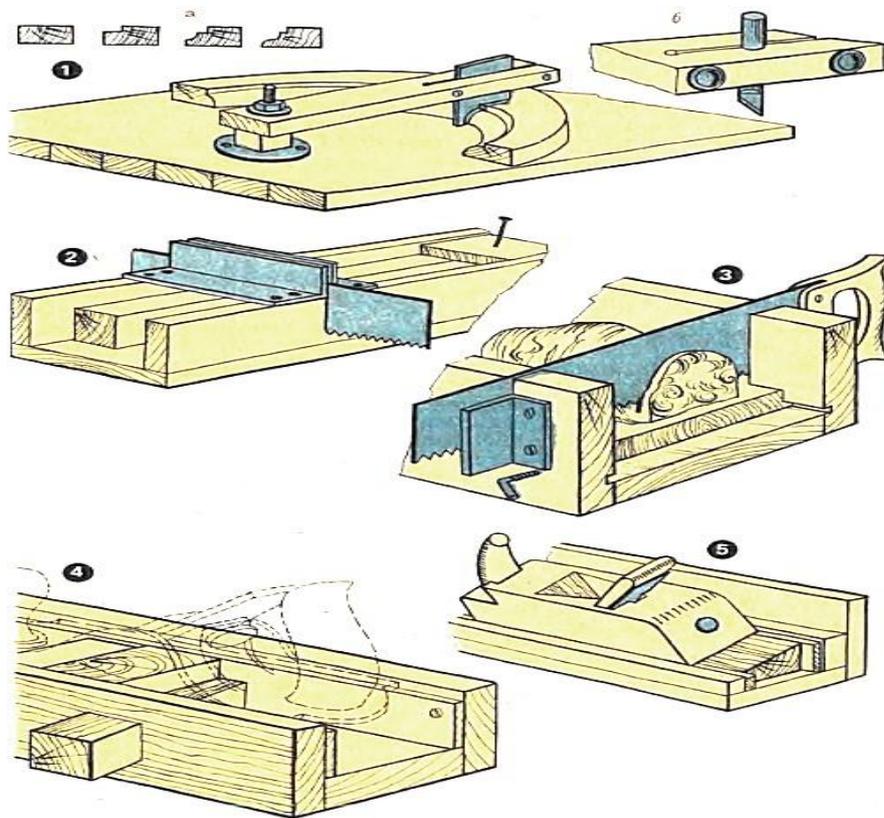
Стусла для обработки деталей: 1 - щитовой столик с воротком для вырезания круговых деталей и профилей; а - порядок обработки профиля; б - крепление ножа в воротке; 2 - стусла для торцевого резания брусков; 3 - стусла для резки каповых дощечек; 4 - стусла для торцевания кубиков; 5 - уголок для застругивания фасок
